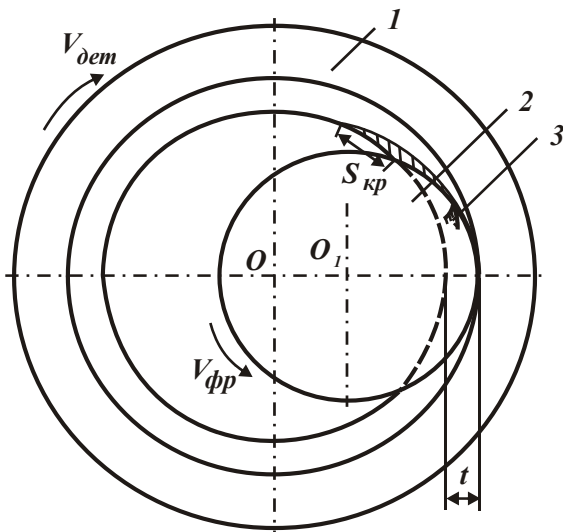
Розрахункова схема параметрів розфрезерування отвору: 1 – оброблюване кільце; 2 – фреза; 3 – зуб фрези
